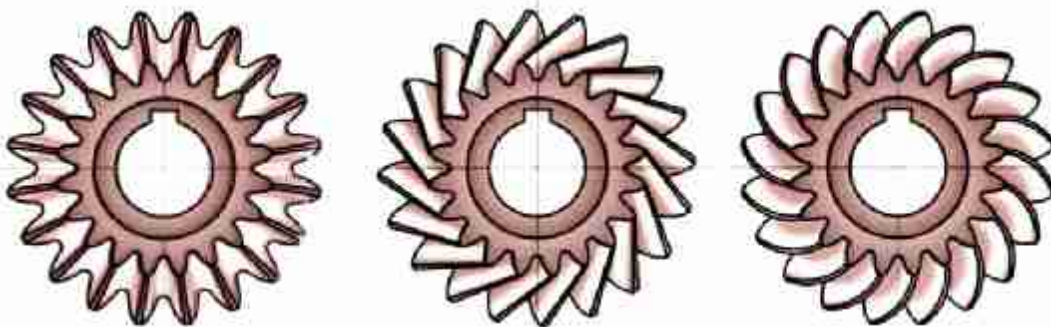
Конические зубчатые колеса с прямыми, тангенциальными, круговыми зубьями
